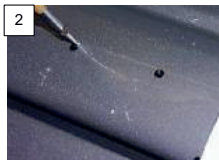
Bohrung der vorderen Befestigungspunkte / Drill the front attachment points
